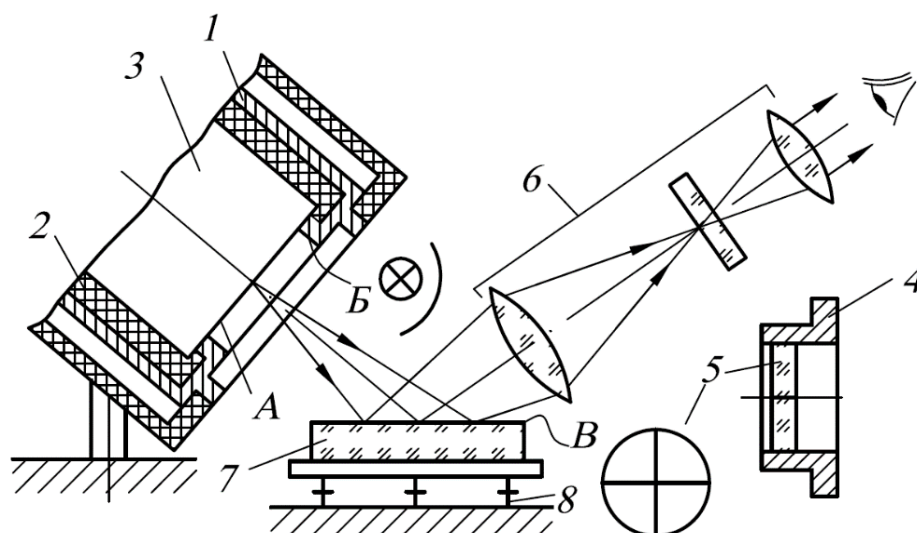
Контрольно-юстировочный прибор для цоколевки ЭОП
